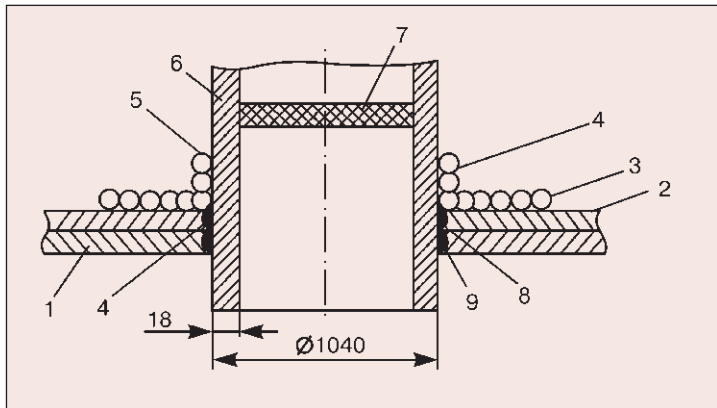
Схема установки электронагревателей КЭН при местной термообработке сварного соединения люк-лаза размером 1040×18 мм: 1 — оболочка шарового резервуара; 2 — воротник люк-лаза; 3 — пояса электронагревателей КЭН на воротнике (первая зона нагрева); 4 — места установки термоэлектрических преобразователей; 5 — пояс электронагревателя КЭН на люк-лазе (вторая зона нагрева); 6 — люк-лаз; 7 — теплоизоляционная заглушка на внутренней полости люк-лаза; 8 — сварные соединения воротника с люк-лазом; 9 — сварное соединение люк-лаза с оболочкой
